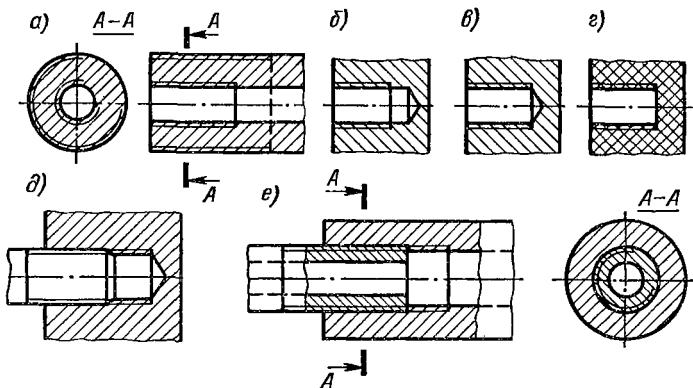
Разрезы и сечения деталей с резьбой и резьбовых соединений
